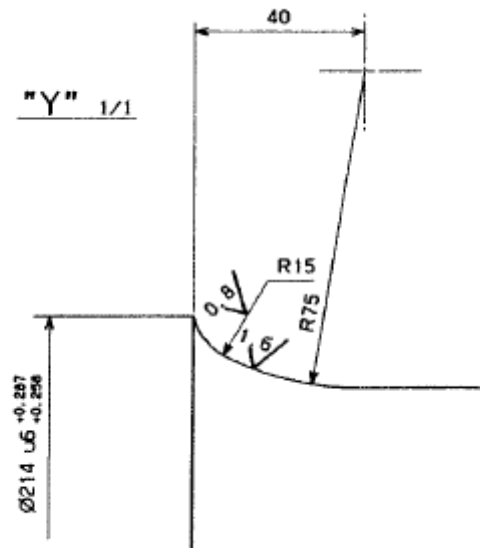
Detalle “Y” del plano del eje ferroviario
